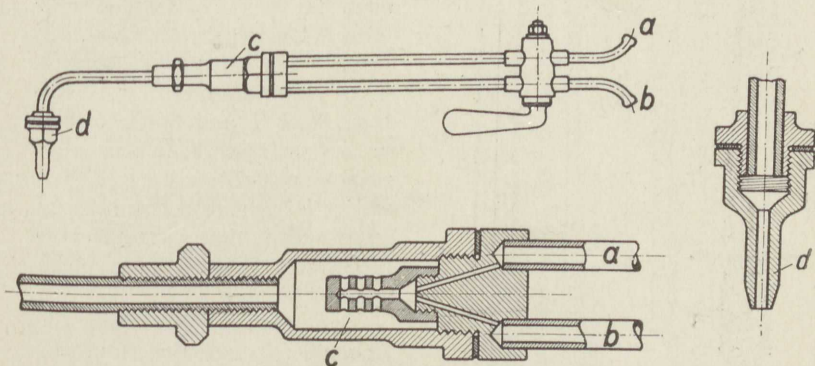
Schweißbrenner für Wasserstoff-Sauerstoff.
